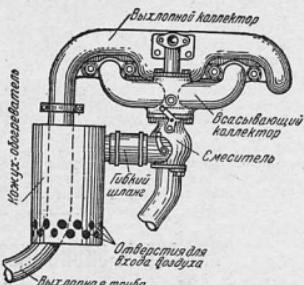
Схема устройства кожуха-обогревателя на автомобилях ГАЗ-42
